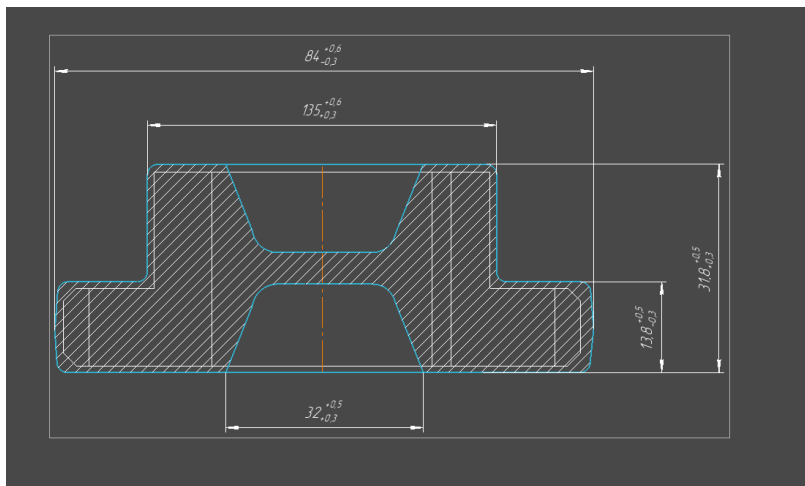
Пример чертежа заготовки ковальной колеса зубчатого
